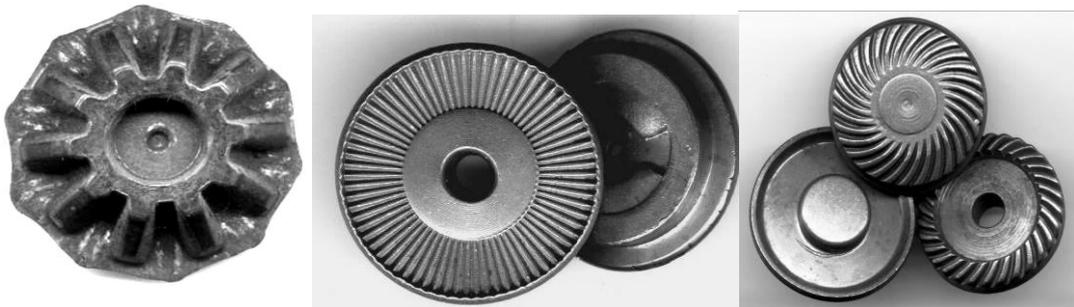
冷摆辗成形的直齿锥齿轮（左）螺旋锥齿轮（中）和兵器零件（右）
